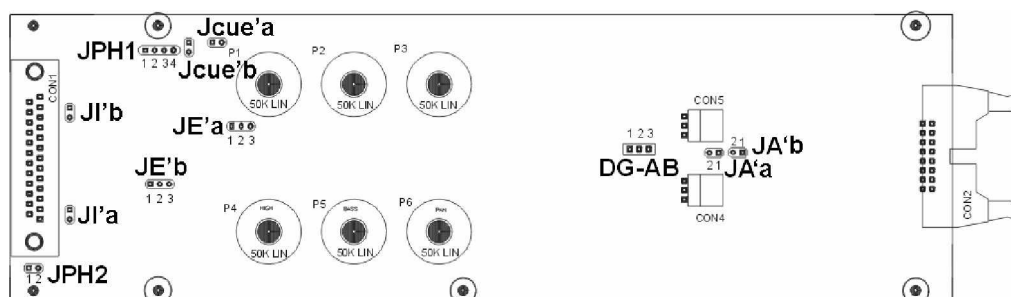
Módulo de micrófono 2310 (vista lado soldaduras)
